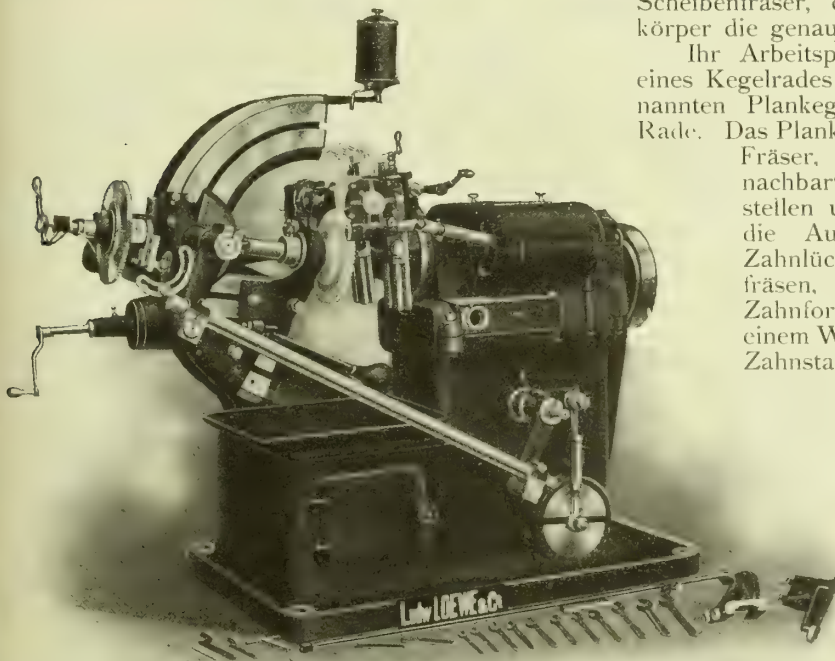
Automatische Kegelräder - Fräsmaschine
